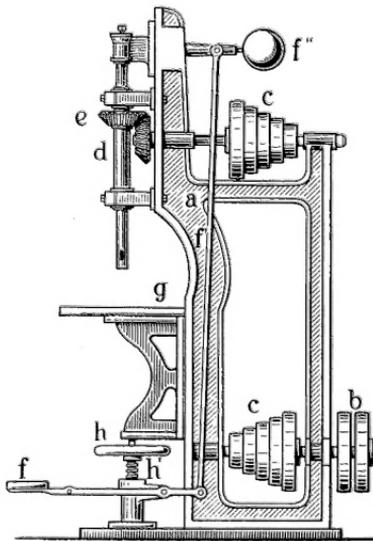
Универсальный вертикально - сверлильный станок. Конструктор Дж. Несмит, 1840 г. По Дж. Ренни
